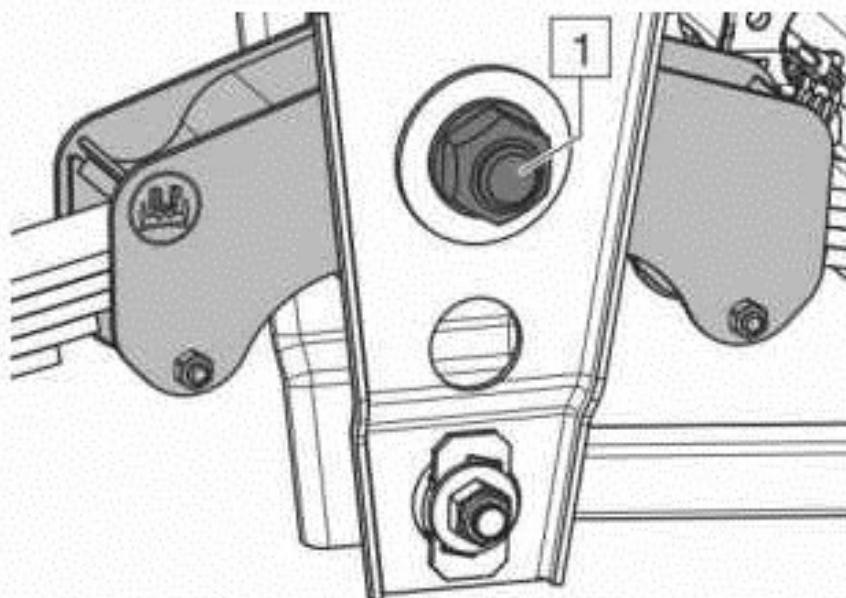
Узел крепления коромысла подвески листового рессора
